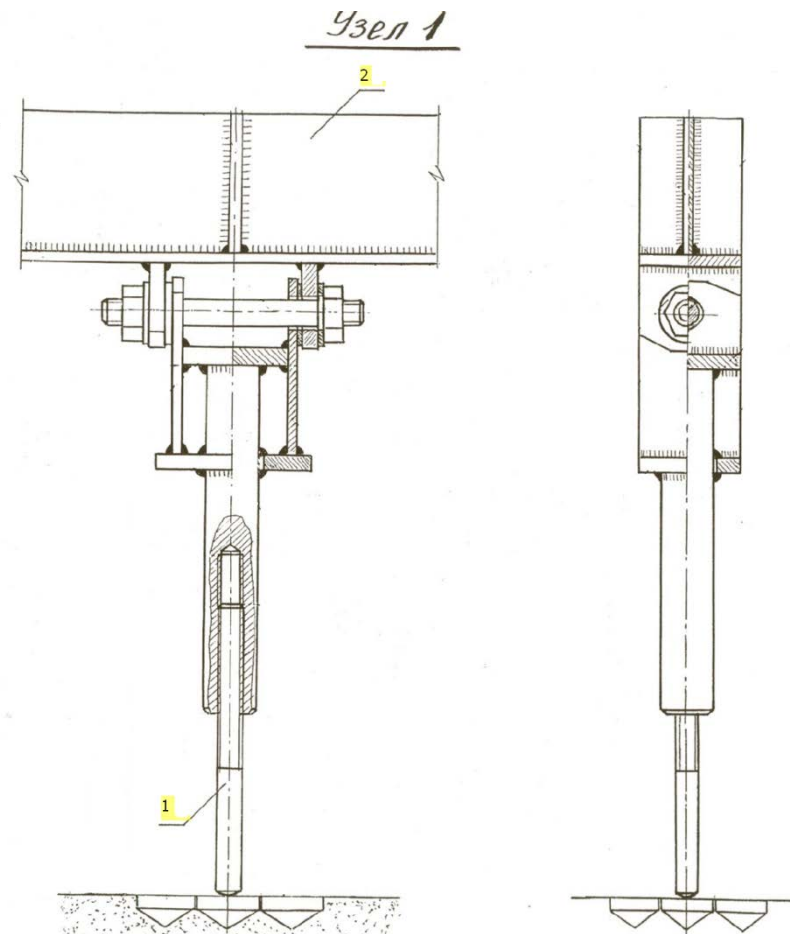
Упорный винт и его крепление к поперечной грузовой балке рычага.
